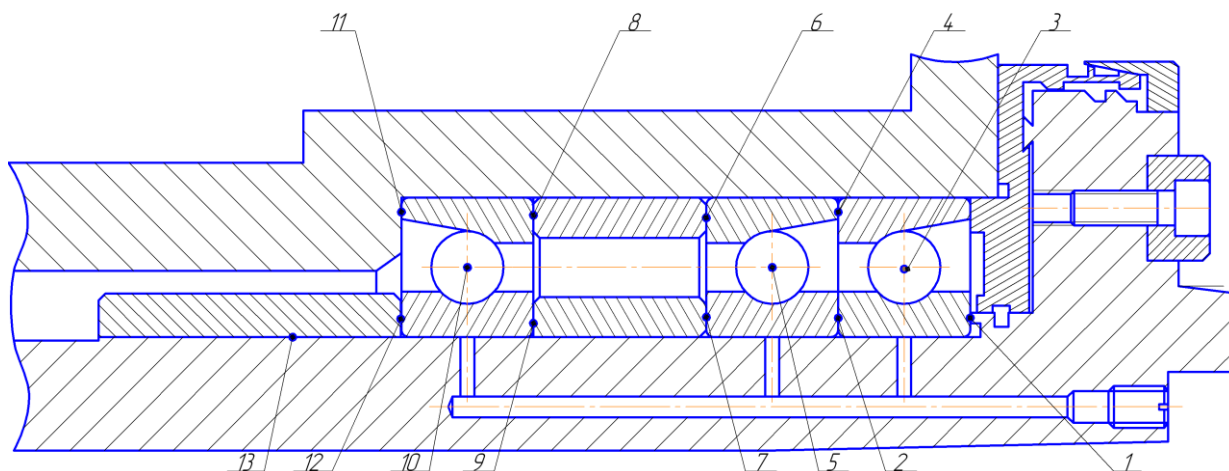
Конструктивна схема передньої опори шпиндельного вузла
